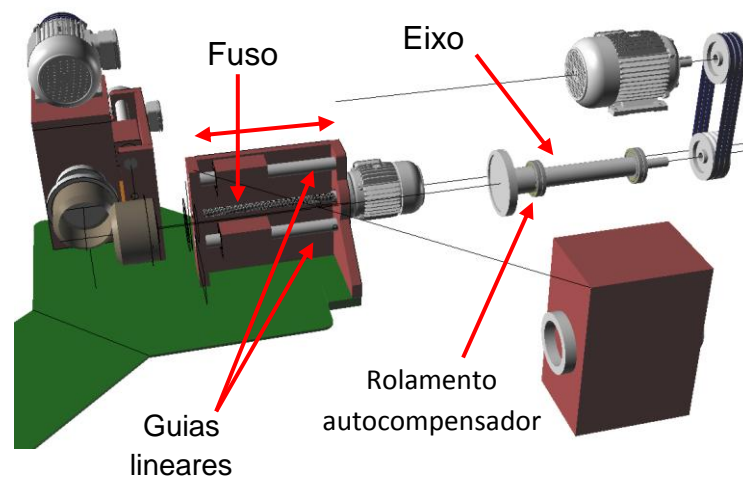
Vista explodida, conjunto de avanço rebolos.
